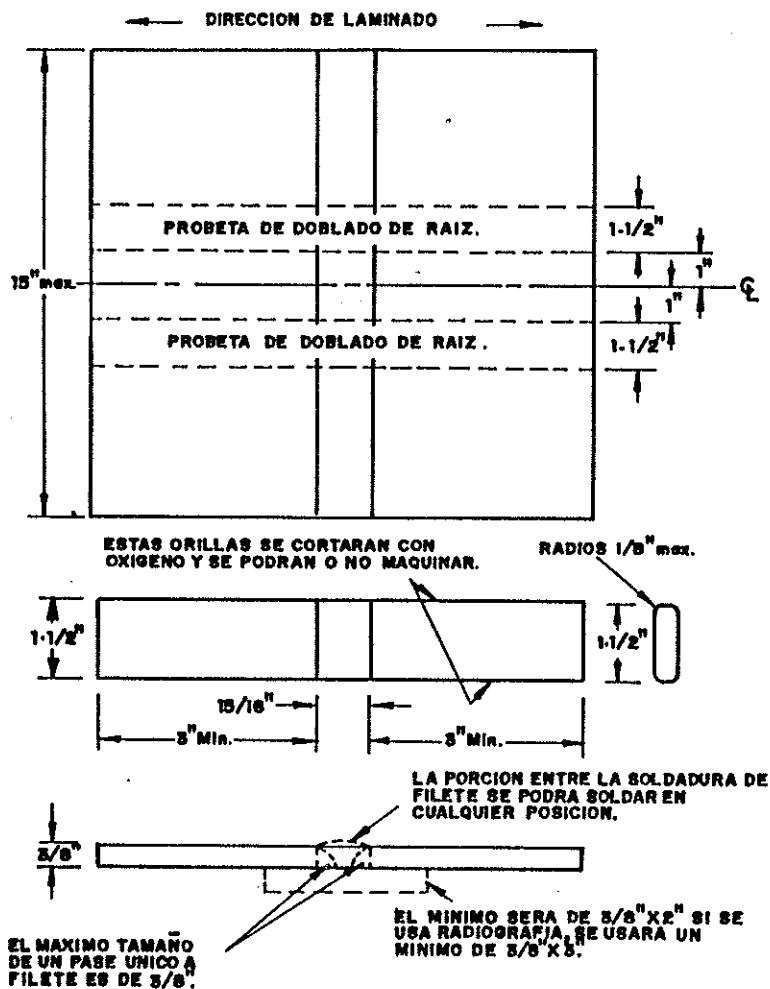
Probeta de ensayo de espesor ilimitado Para calificación de Operadores de soldadura.
